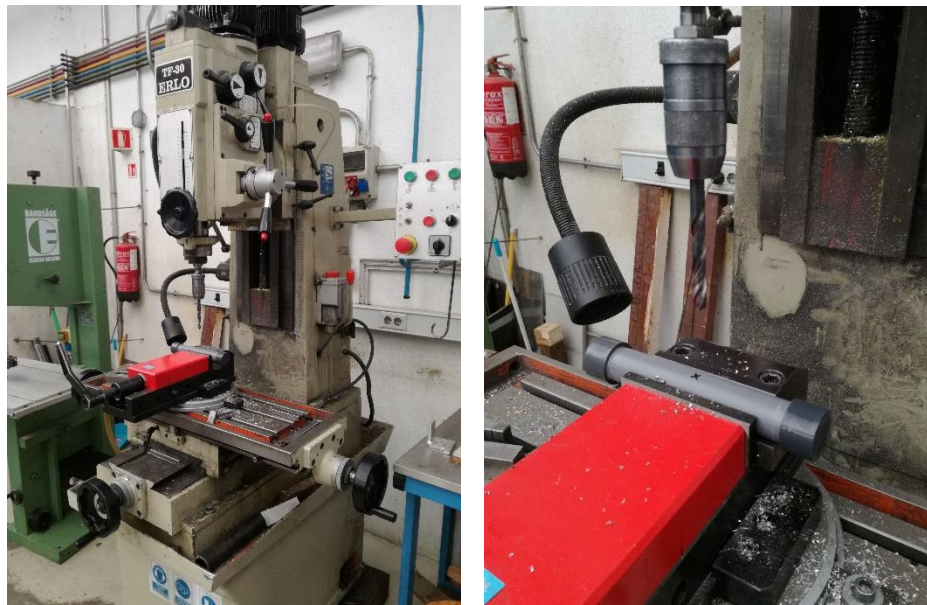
Vista general de la taladradora-fresadora y detalle de la posición del molde.
